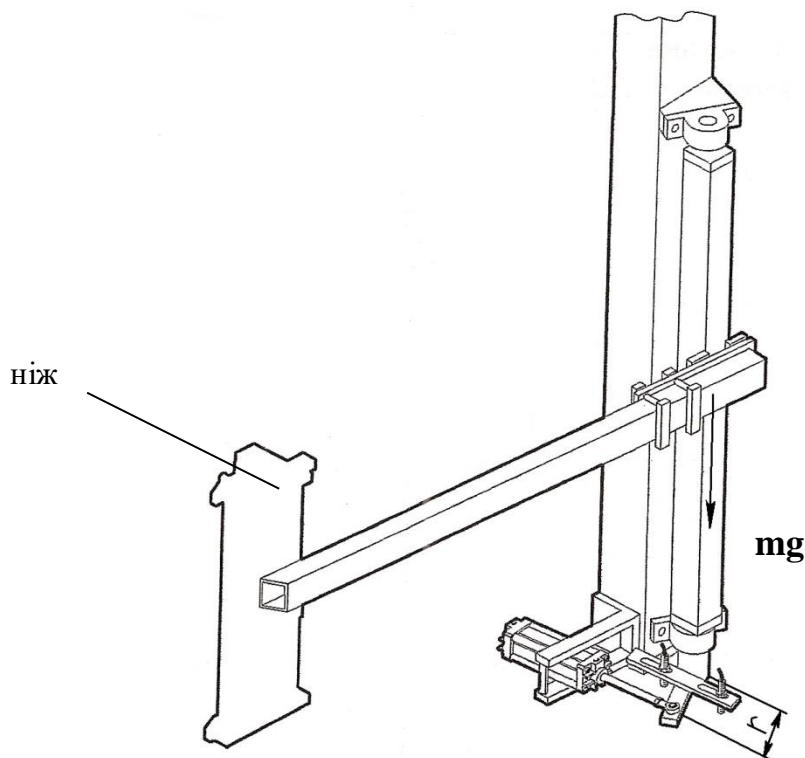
Розрахункова схема для механізму відрізання полімерної розтягувальної плівки
